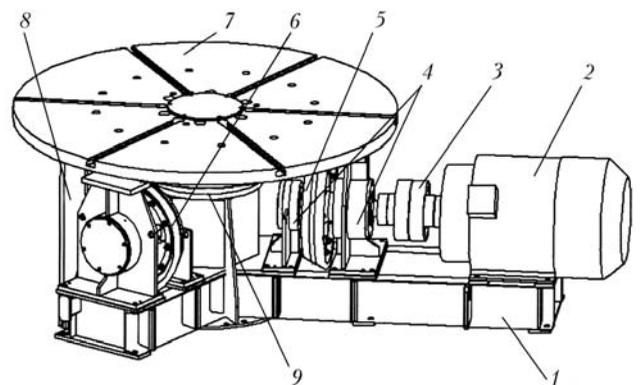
Конструкция центробежной машины: 1 – станина; 2 – электродвигатель; 3 – муфта соединительная; 4 – узел подшипниковый; 5 – каток ведущий; 6 – каток ведомый; 7 – планшайба; 8 – щиток защитный; 9 – узел подшипниковый центральный
